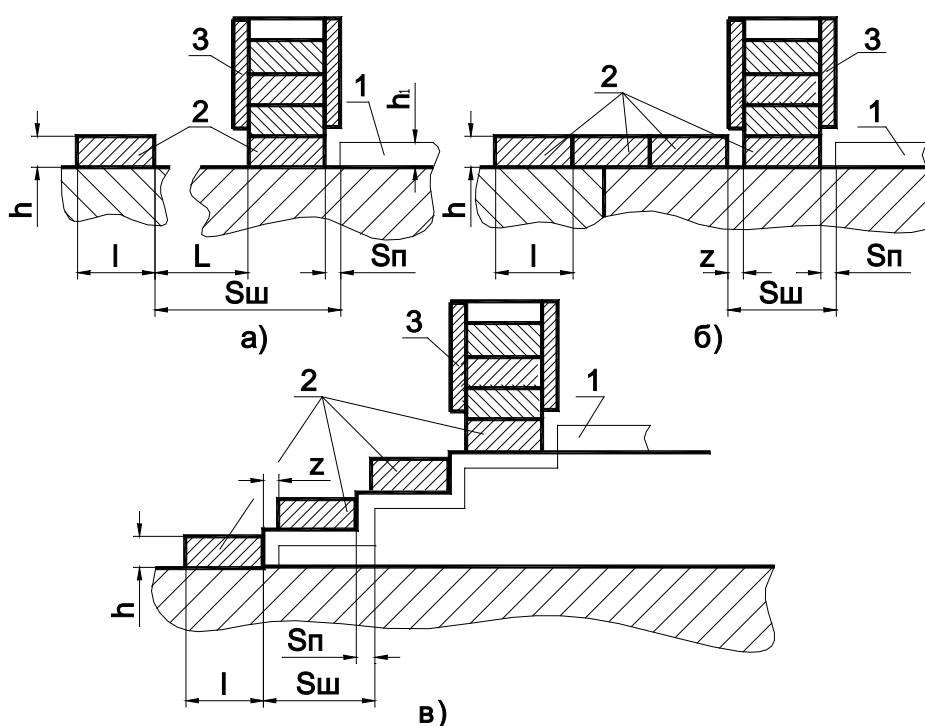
Схемы способов подачи заготовок. 1 - шибера, 2 - заготовки, 3 - магазин
